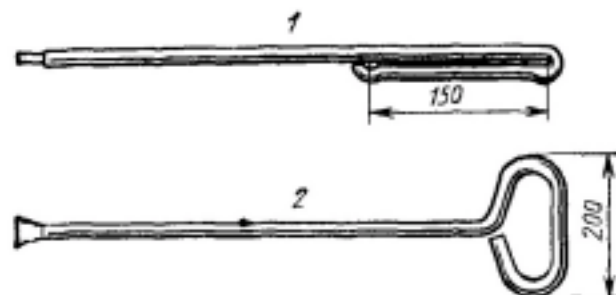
Ручки кузнечного инструмента дляковки металла на молотах
